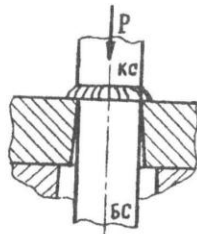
Схема удаления сварочного гра-та штамповкой
